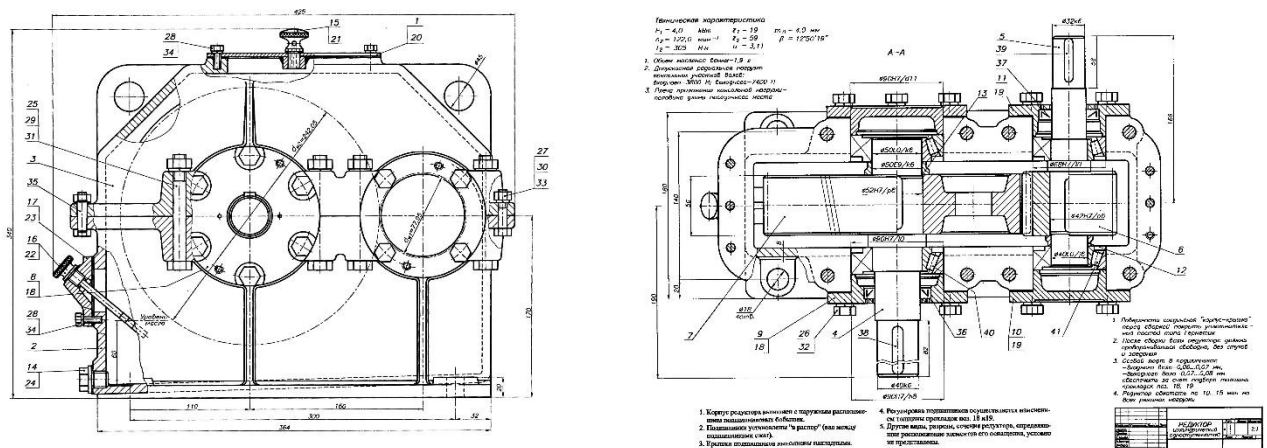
Цилиндрический одноступенчатый редуктор
